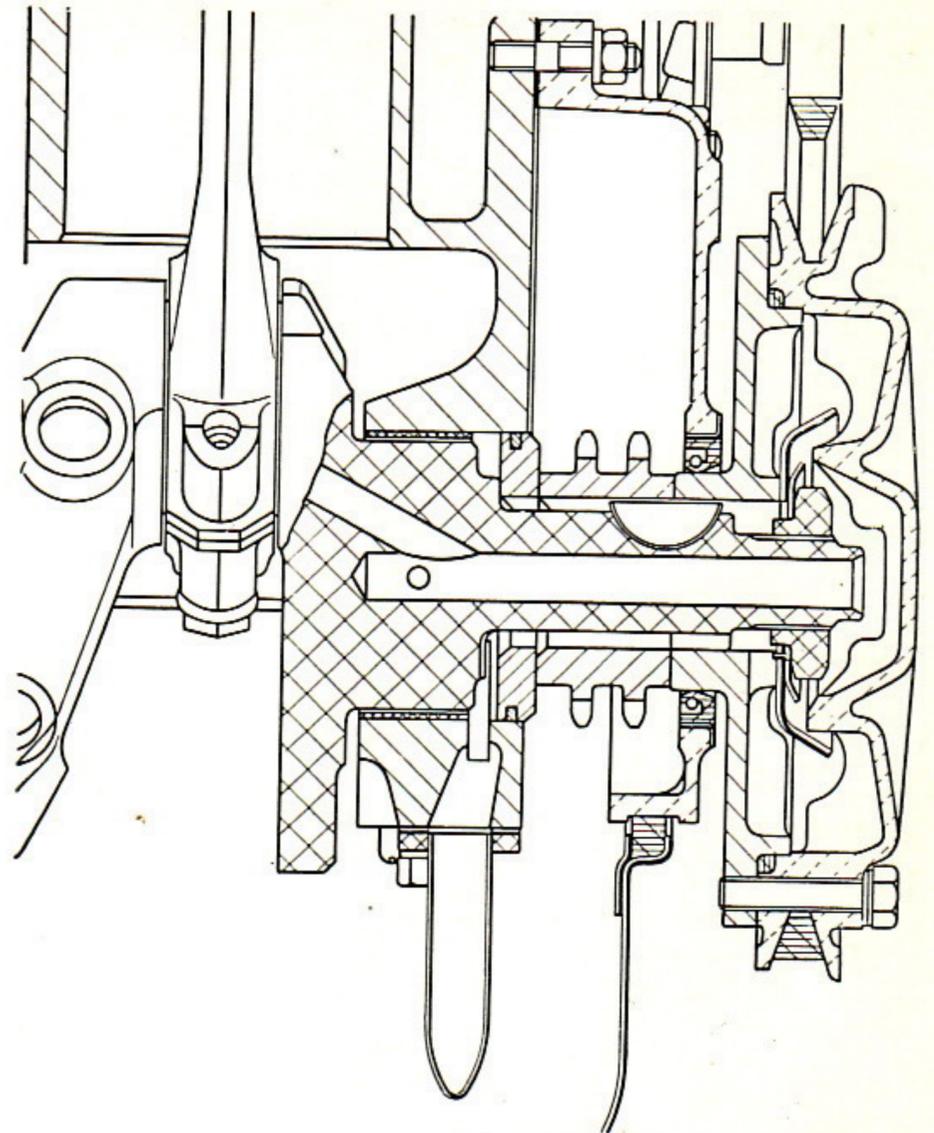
Sezione longitudinale del motore, particolare sul filtro olio centrifugo.
